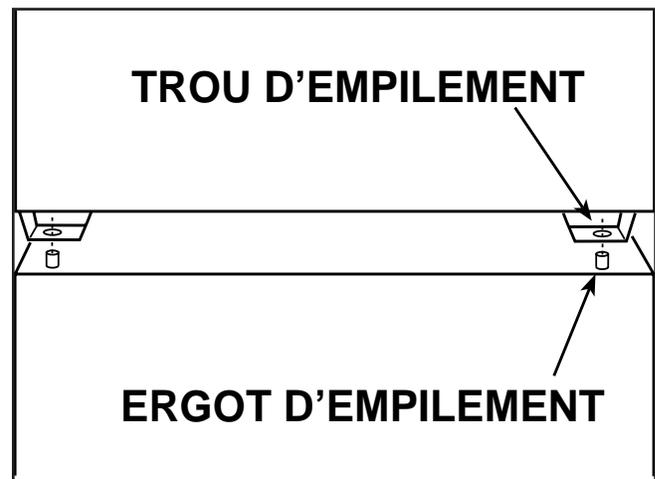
EMPILEMENT DES MACHINES DC-600
